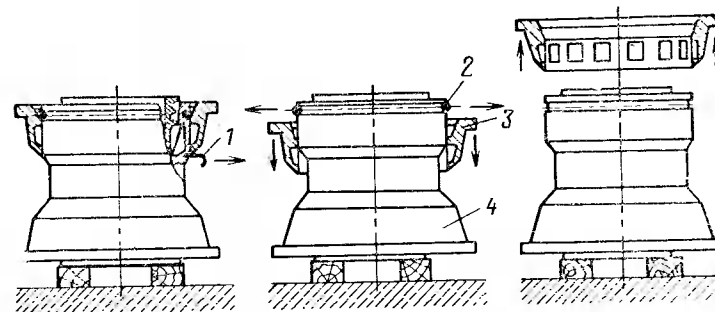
Монтаж пневматика на неразъемное колесо: 1 — стопорный штифт; 2 — полукольцо; 3 — съемный борт; 4 — барабан
